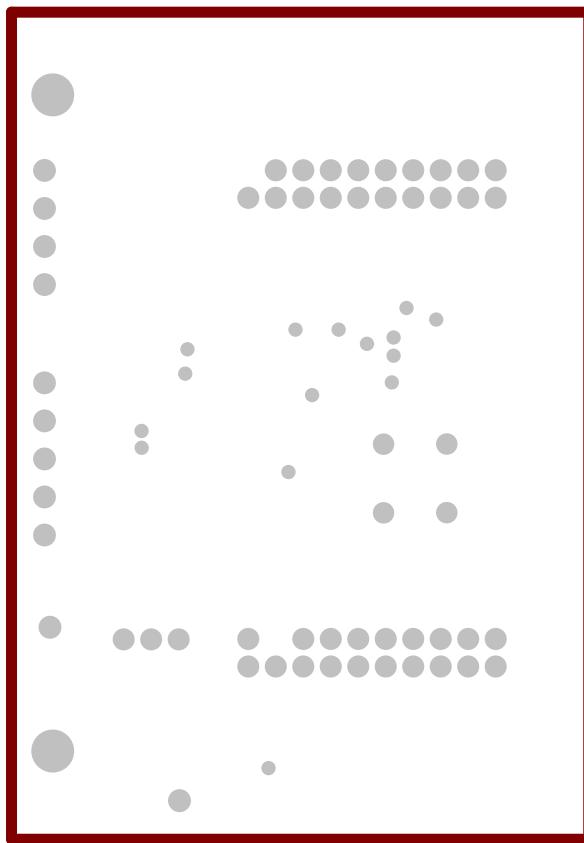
ADS122x14EVM の PCB レイアウト (内部 GND プレーン 2)
